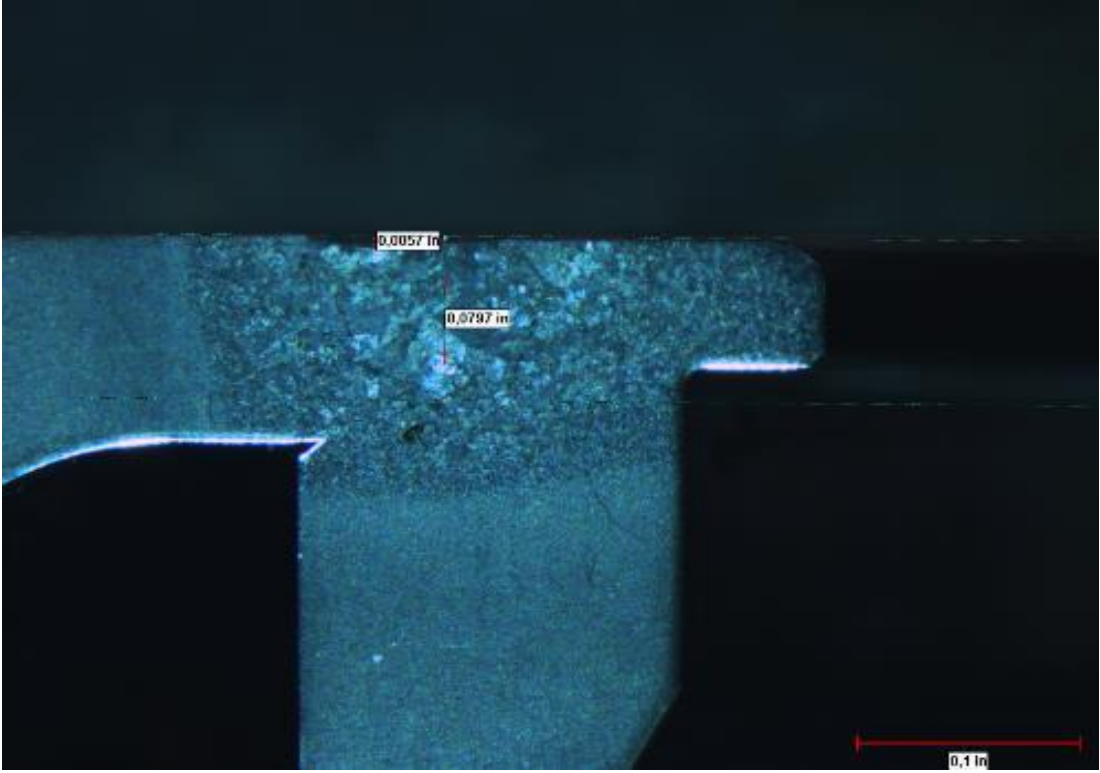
Kupon 2 kesiti makro görüntü (KN: 1.08, KYÇ: 0.15) / Kaynak bölgesi 2
